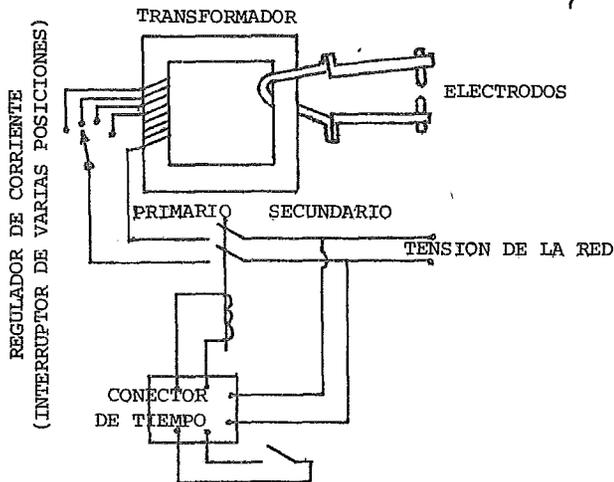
FUNDAMENTO DE LA SOLDADURA POR RESISTENCIA ELECTRICA
